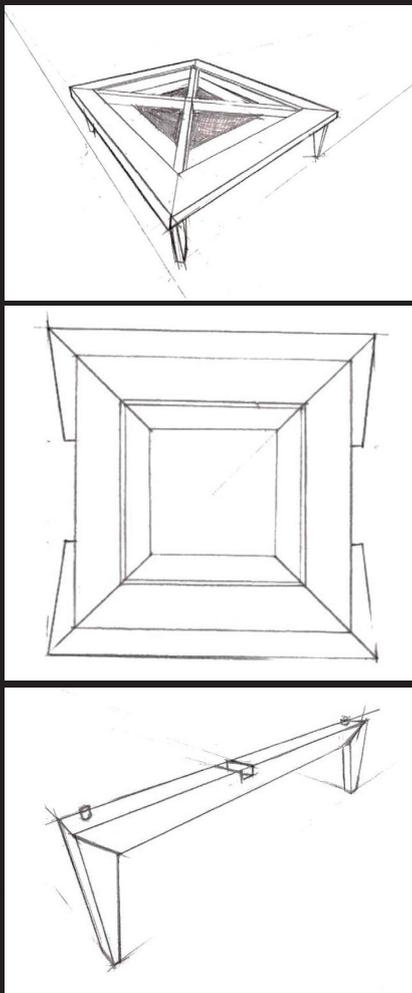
Sketches manuais com a definição tridimensional do conjunto, a planificação dos componentes e o detalhamento dos encaixes entre as peças.
